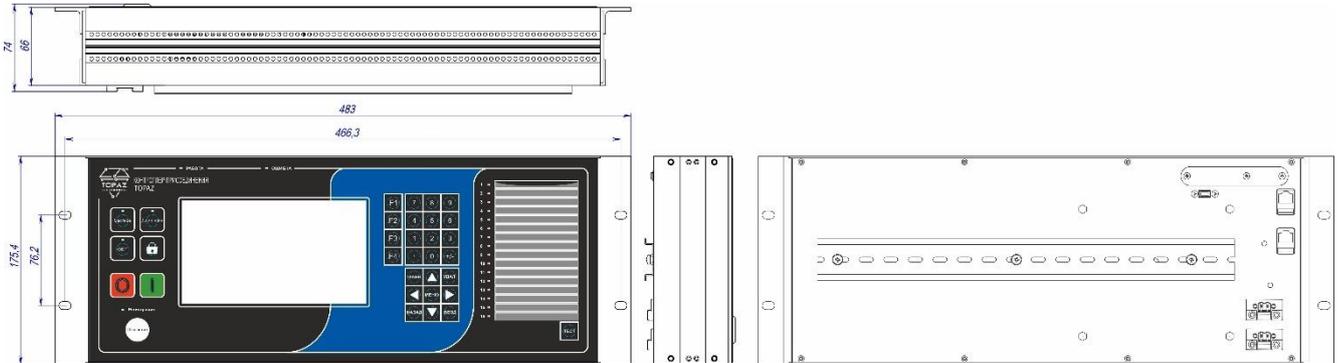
Внешний вид и габаритные размеры панели TOPAZ HMI
